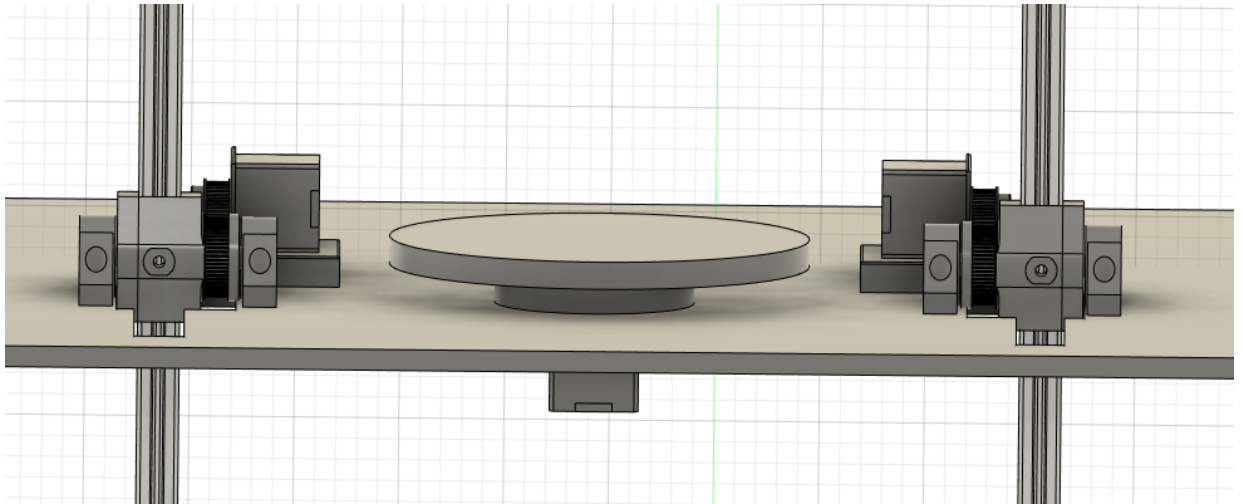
3D-модель механічної конструкції робочої поверхні
